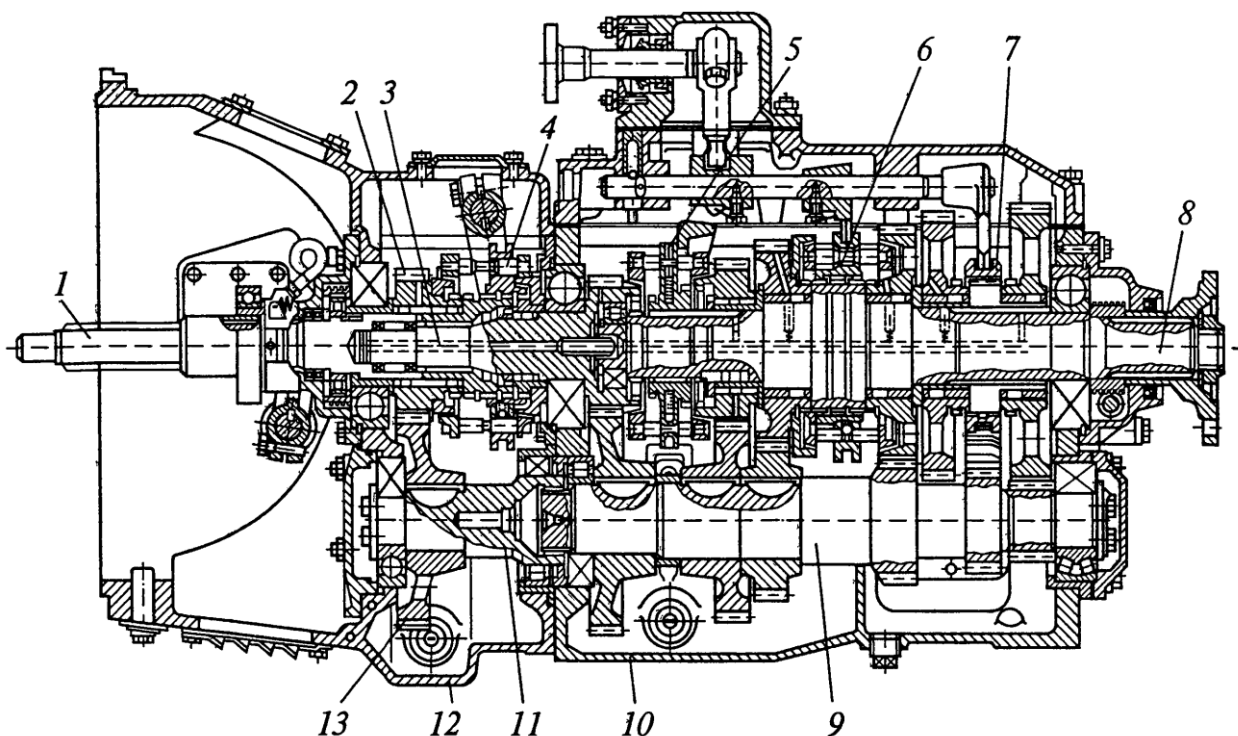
Коробка перемикання передач автомобіля КамАЗ: 1 – ведучий вал; 2, 13 – шестерні; 3 – первинний вал; 4, 5, 6 – синхронізатори; 7 – муфта; 8 – вторинний вал; 9, 11 – проміжні вали; 10, 12 – картери
